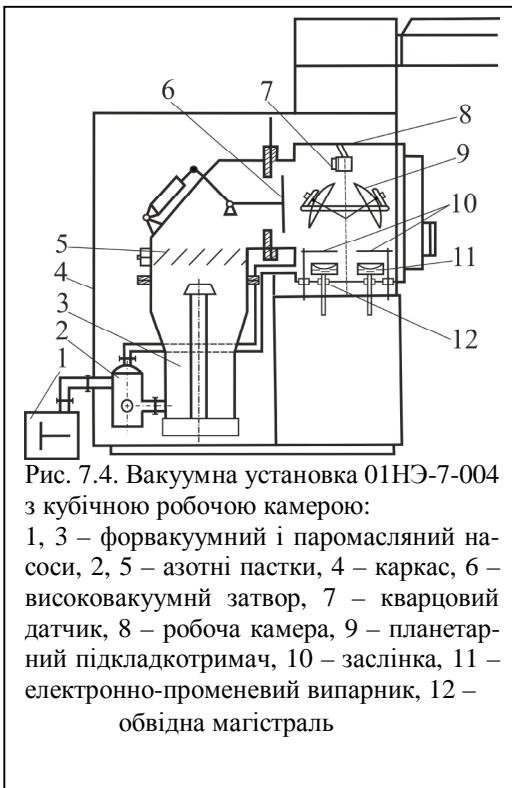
Вакуумна установка 01НЭ-7-004 з кубічною робочою камерою:
